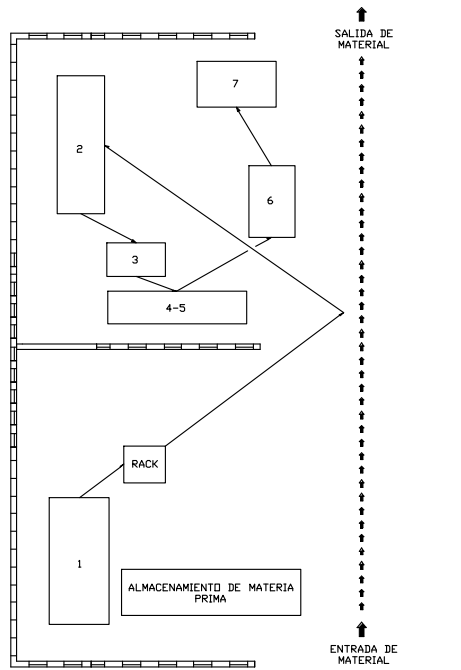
Plano General de la Planta de Doblado de Tubos.
